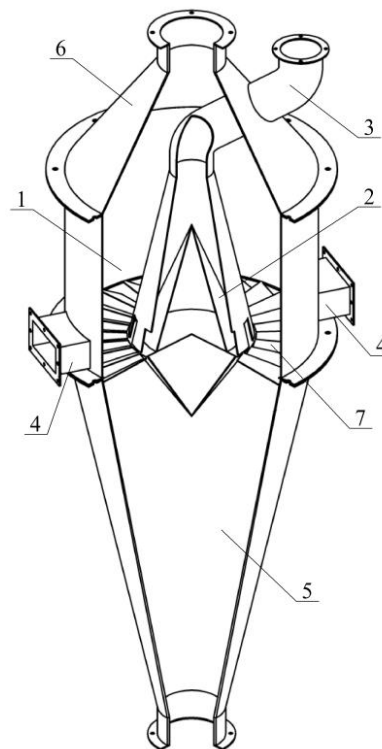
Схема лабораторного аппарата с центробежным псевдооживленным слоем: 1 – рабочая камера; 2 – внутренняя стенка; 3 – загрузочное устройство; 4 – разгрузочные окна; 5, 6 – газовые камеры; 7 – газораспределительное устройство
